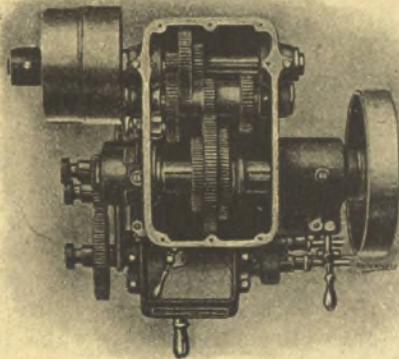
Vue du carter de la poupée fixe, ouvert, montrant les *trains baladeurs à bain d'huile*.
